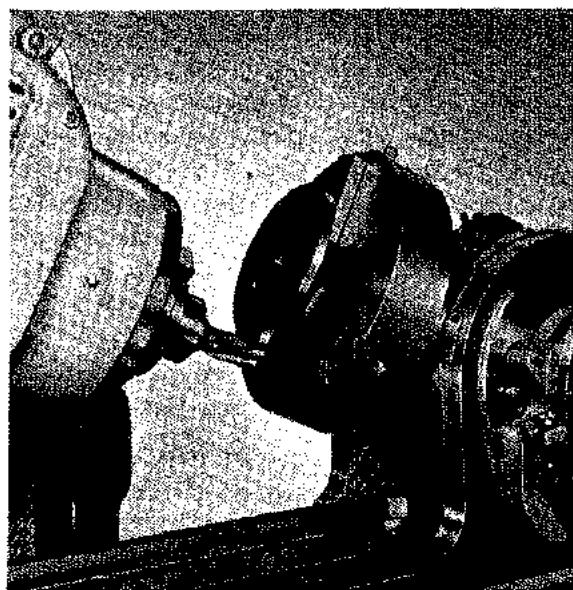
Fresado de una leva de elevación uniforme con el aparato de husillo vertical y el accesorio de avance largo y corto (Cincinnati Milling Machine Co.)
